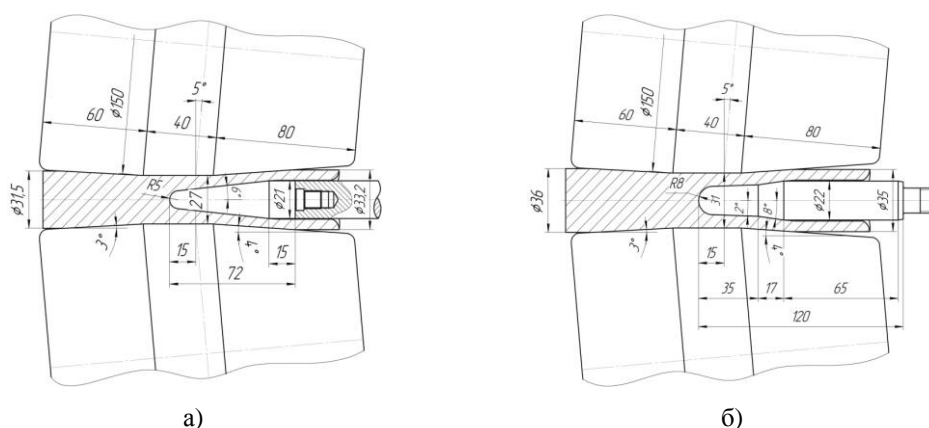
Схема очага деформации при прошивке заготовок:
